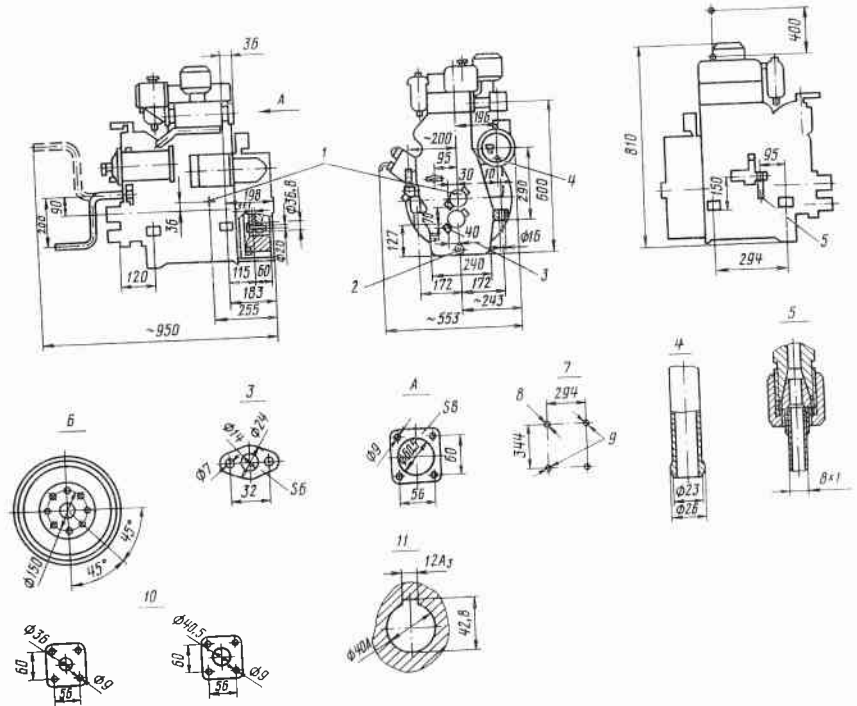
Габаритный чертеж дизелей 5Д2 и 5Д2-1:
